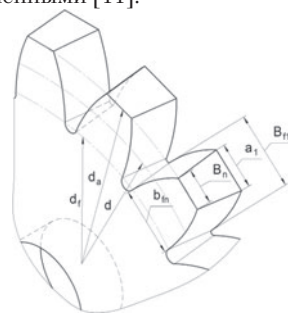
Зубчатый венец цилиндрического конусно-клинового зубчатого колеса
